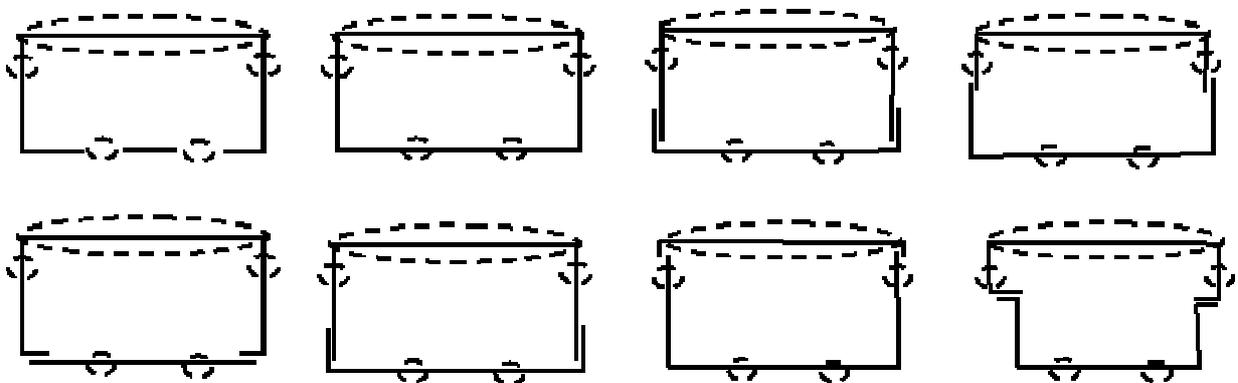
Modulare Konstruktionsvarianten einer Kastenstruktur
